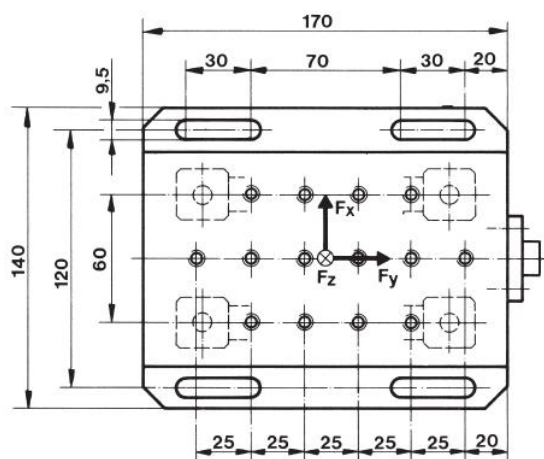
Kistler Multikomponent Force Plate – Typ 9253B [14].
